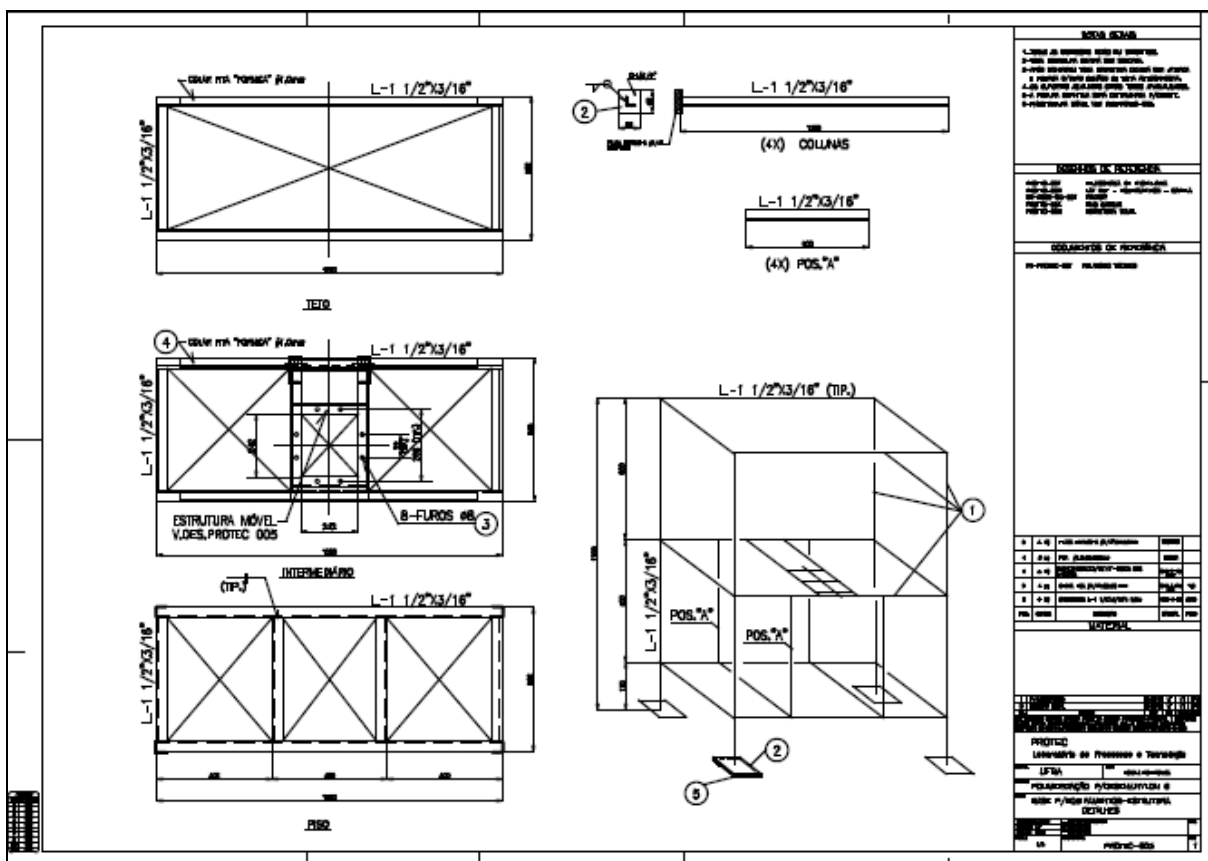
Desenho mecânico construtivo da parte fixa da estrutura de sustentação, com detalhes de montagem da estrutura móvel.
